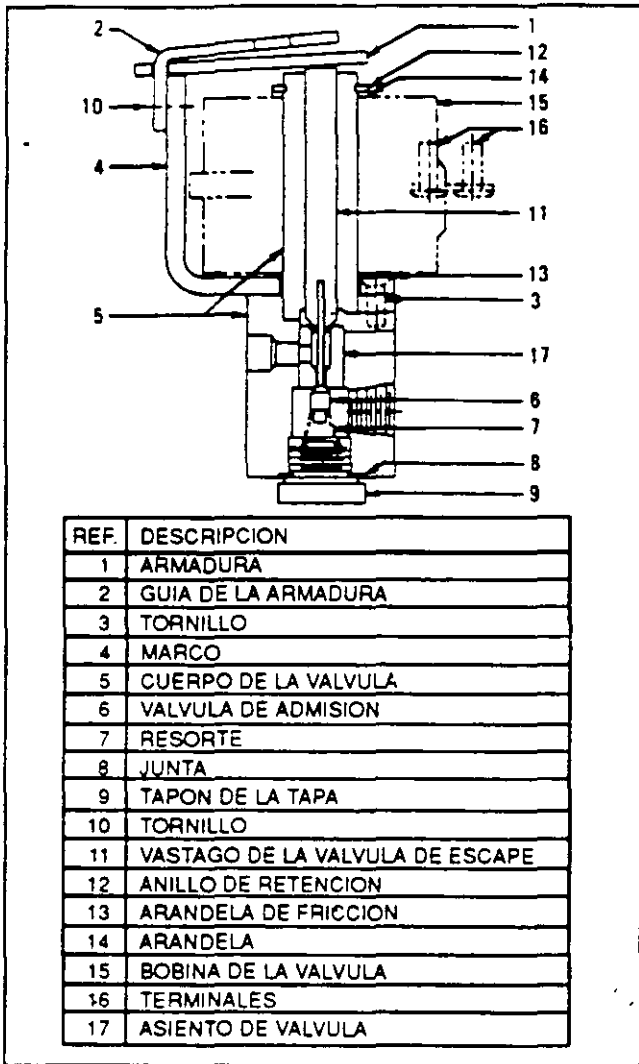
VISTA EN CORTE DE LA VALVULA MAGNETICA MV38. E-10645-S
